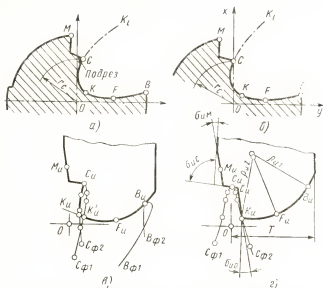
Форма профиля фрезы и канавки сверла при различных значениях параметров установки фрезы
